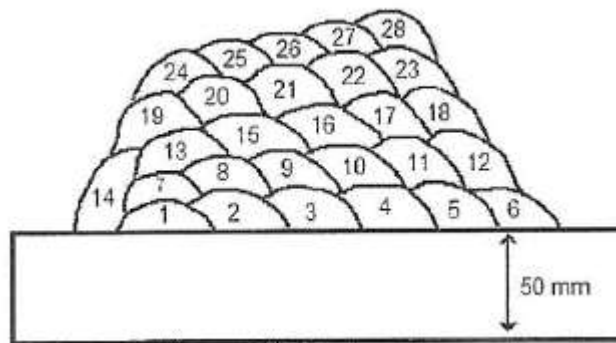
Detalhamento da junta soldada referente a EPS-005. Fonte: autor
